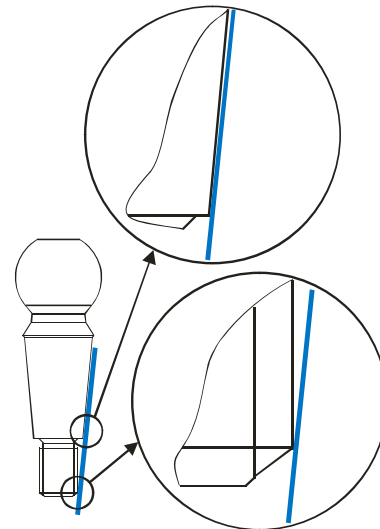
Damit auch am Gewinde Kontakt bestand (unterer Ausschnitt), musste die Probe leicht gekippt werden, wodurch die Kontaktfläche am Konus jedoch sehr stark eingeschränkt wurde (oberer Ausschnitt)
